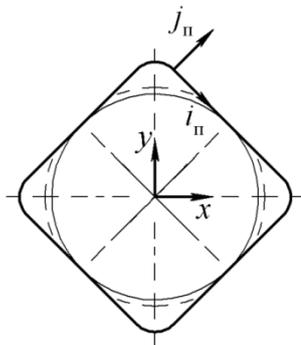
Выбор систем координат СМП леворежущего инструмента
